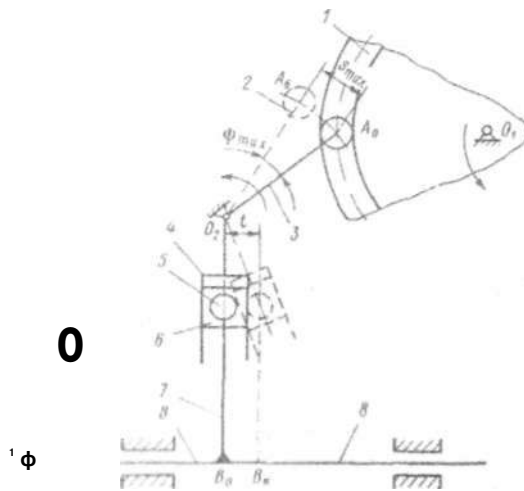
Схема механизма каретки пуговичного полуавтомата
